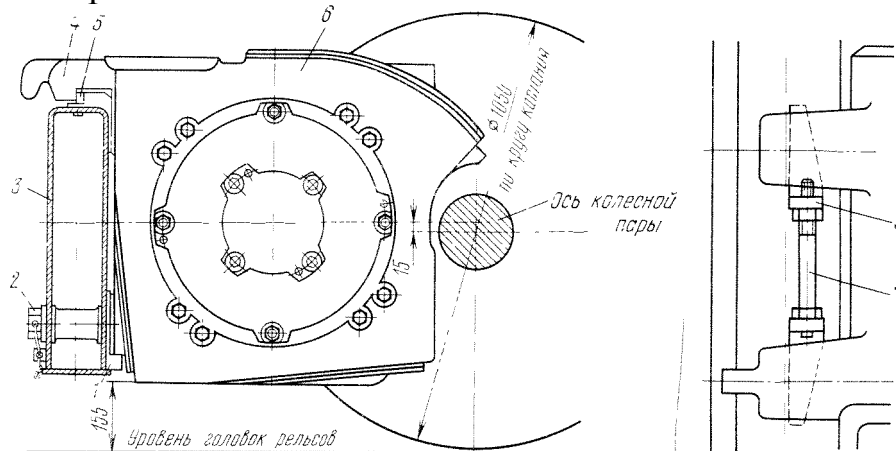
Крепление тягового двигателя на раме тележки моторного вагона
